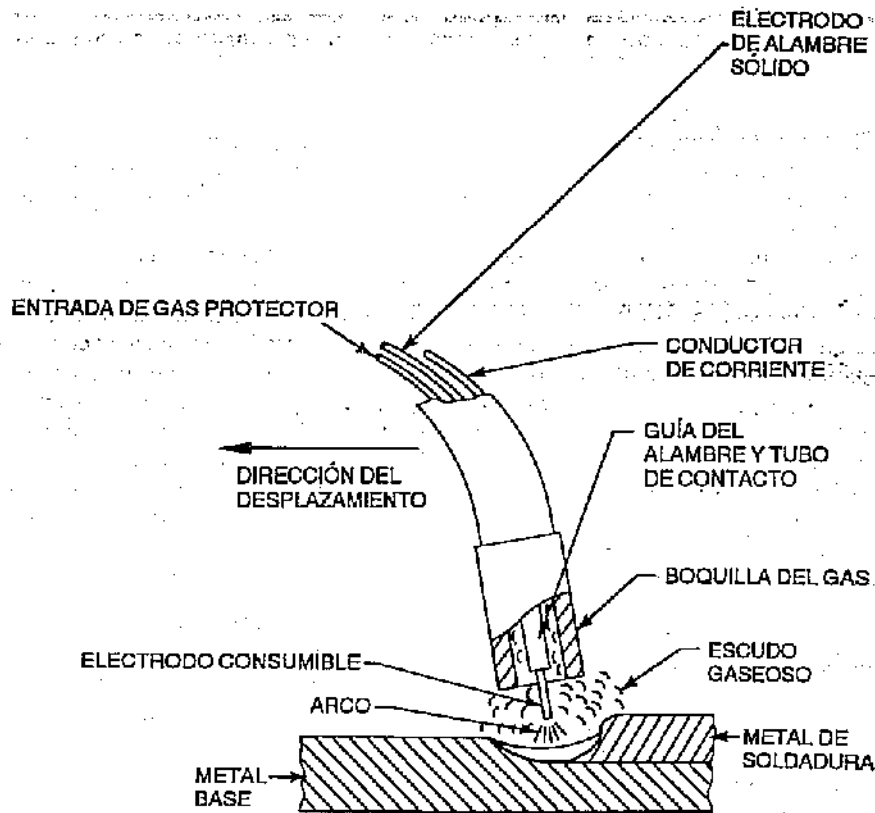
Proceso de soldadura por arco de metal y gas
